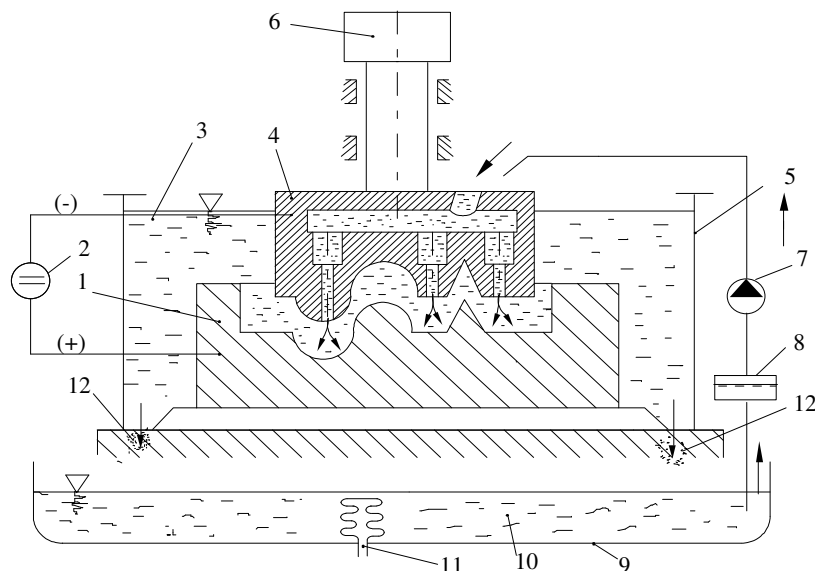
Schema de principiu a unei instalații de prelucrare dimensională prin electrochimie cu cap vertical:
